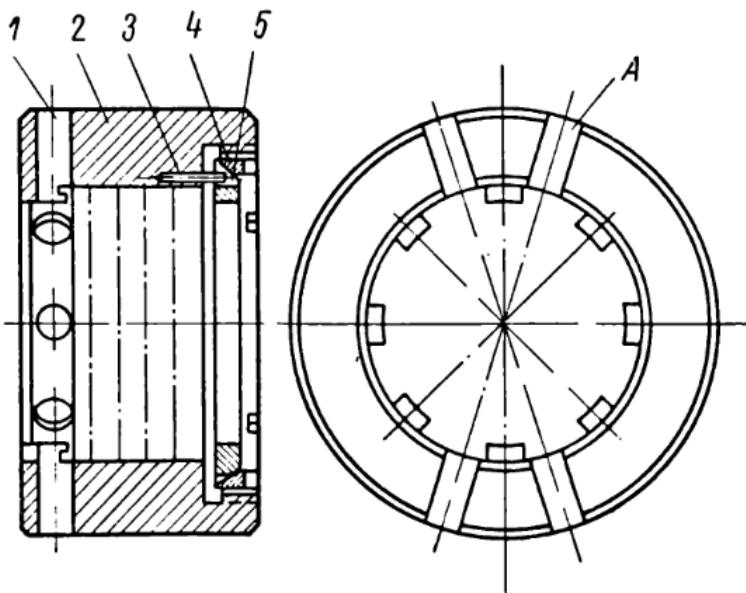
Стакан для крепления тонкостенных и узких деталей типа колец
